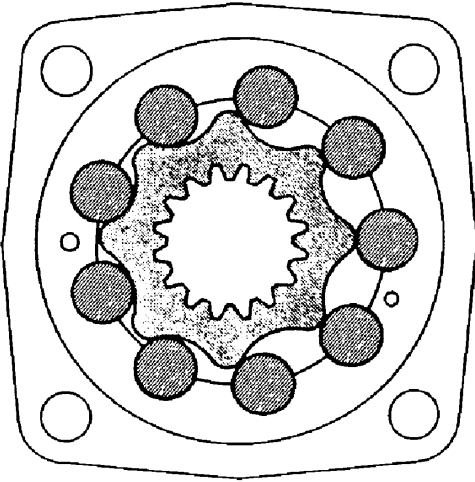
Планетарный гидромотор с роликовыми зубьями
